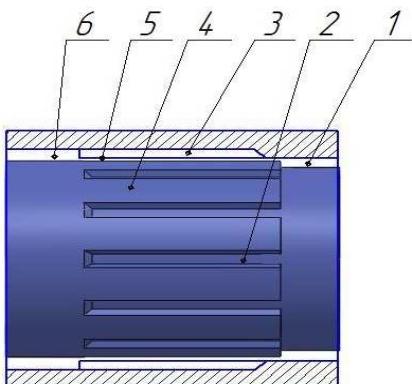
Динамічний змішувач: 1 – вхідний кільцевий канал; 2 – вхідне поглиблення ротора; 3 – вихідне поглиблення корпусу; 4 – бар'єрний гребінь ротора; 5 – бар'єрний гребінь корпуса; 6 – вихідний кільцевий канал
